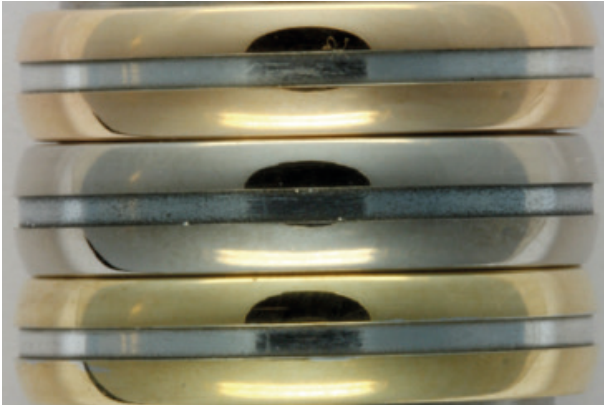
| Ringe aus 18kt Goldlegierungen mit Blaugoldbeschichtung
